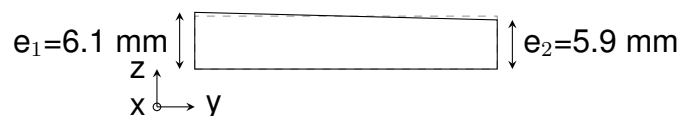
Section trapézoïdale dans le plan (yz)
